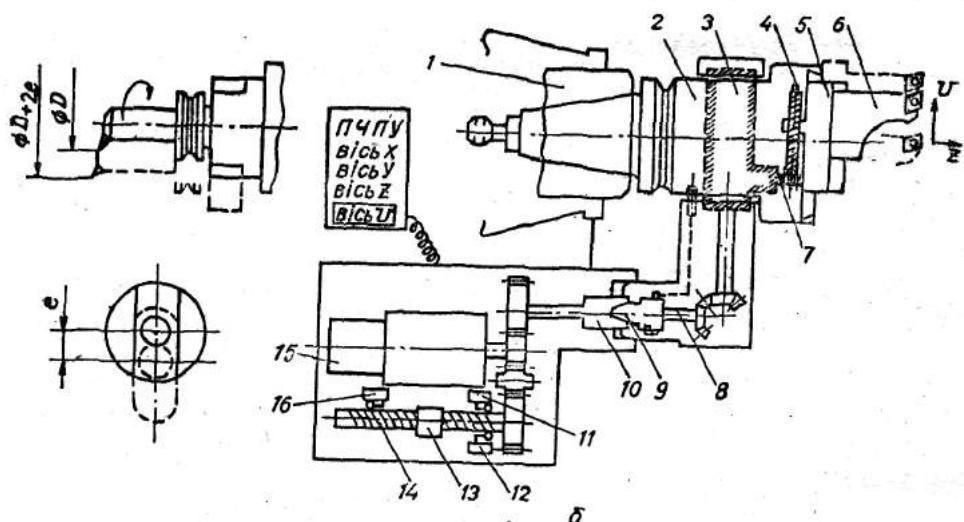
Схема план-супортної головки (а) та її конструкція (б):
